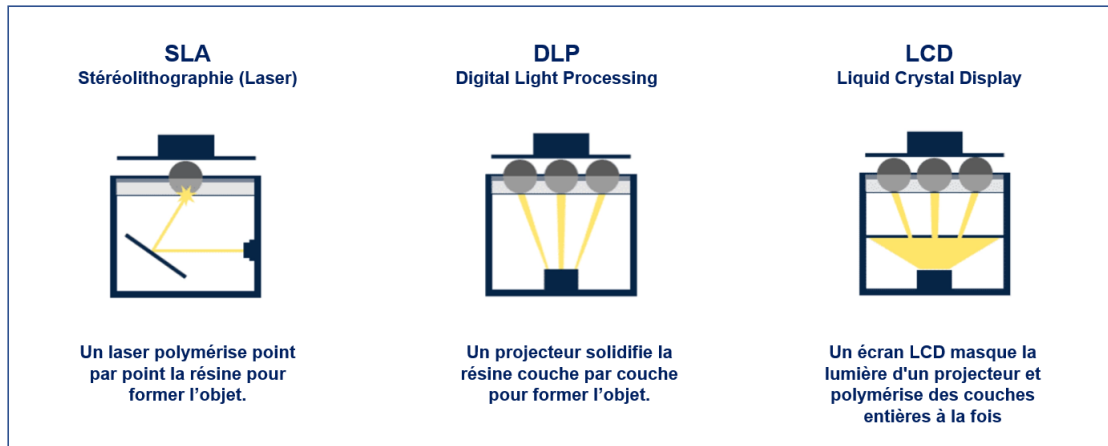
Principales technologies des imprimantes 3D résine [83].
